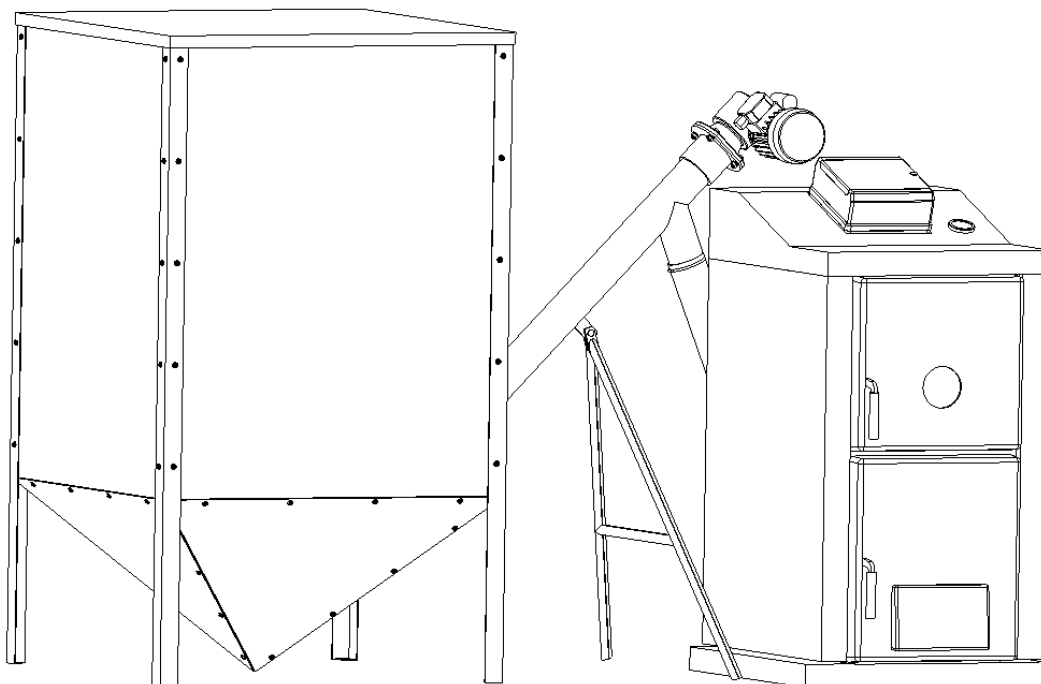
Vue avant de la chaudière CEDRA ECO avec trémie - version gauche
